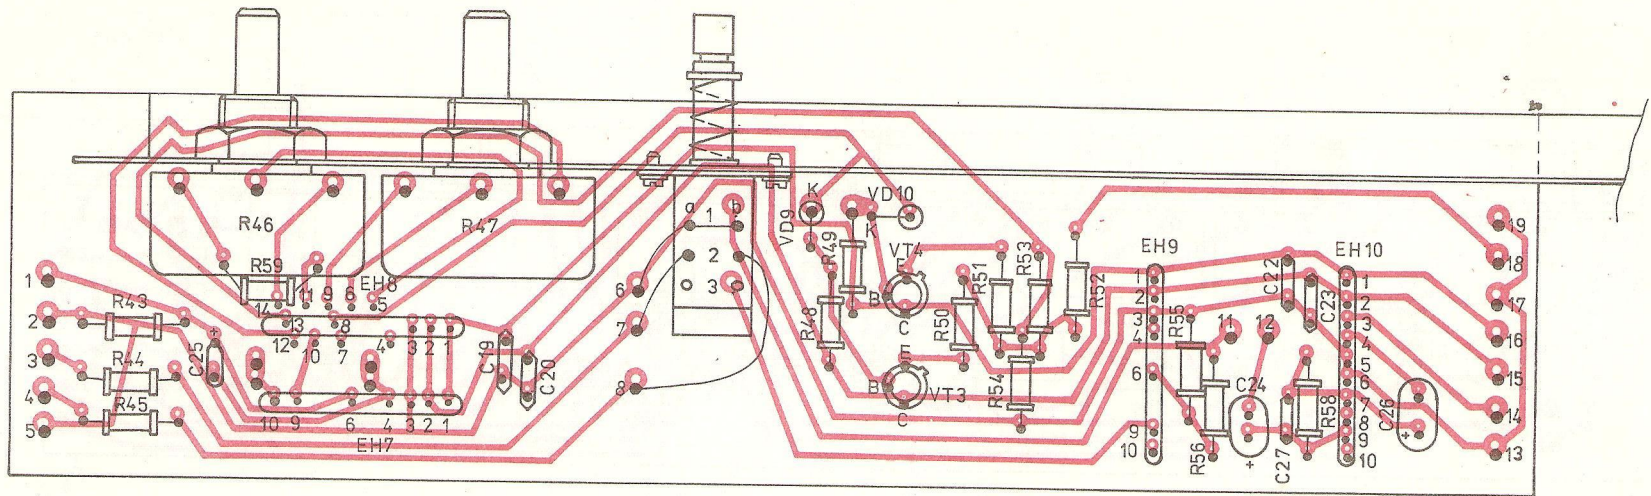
Schéma zapojení desky zdrojové 3AK 061 41
